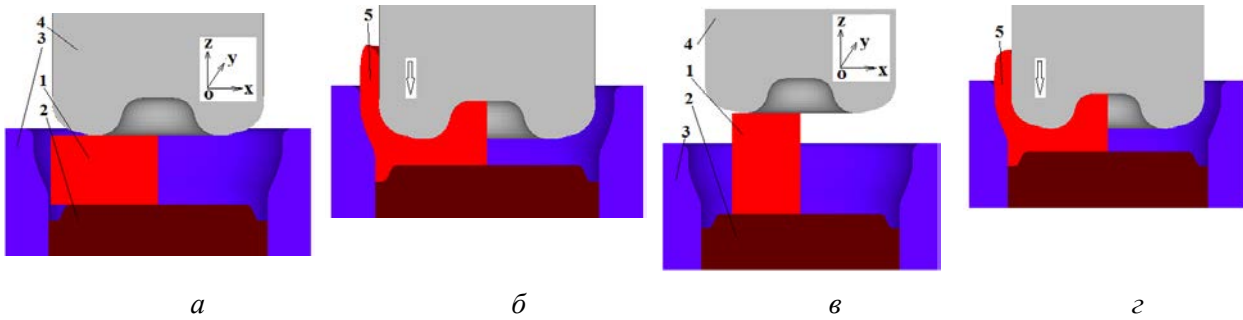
Розрахункові схеми на початку і в кінці видавлювання: *a* і *б* – заготовки круглого перерізу; *v* і *z* – заготовки квадратного перерізу
